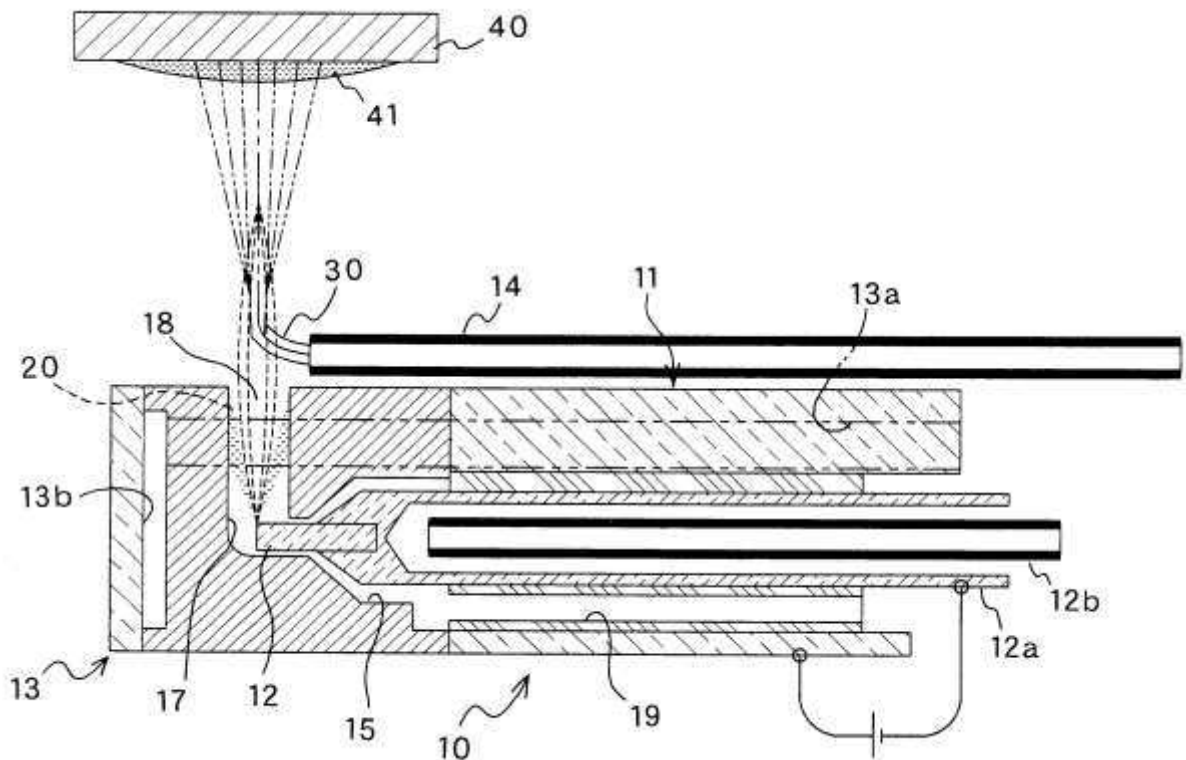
"Факел головка для плазменного напыления" схематичное изображение
